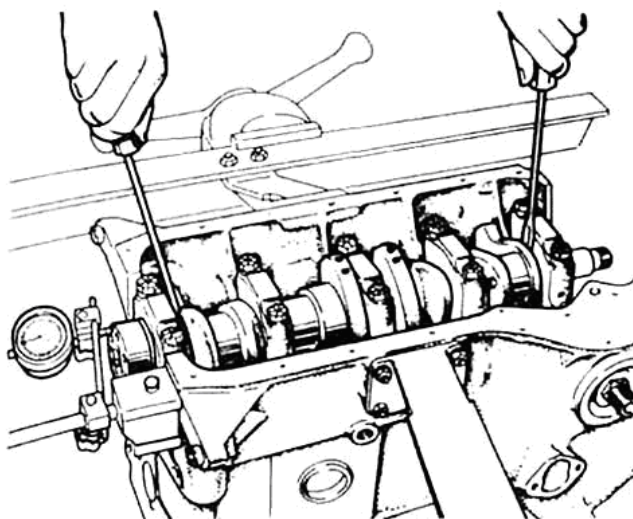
Проверка осевого зазора КВ с помощью двух отверток и индикатора часового типа
